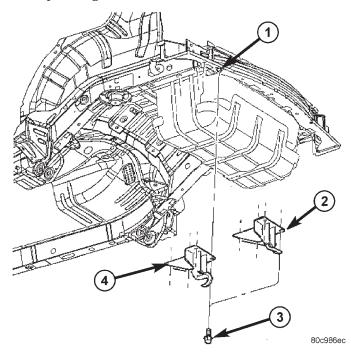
GANCHO/ANILLA PARA REMOLQUE
